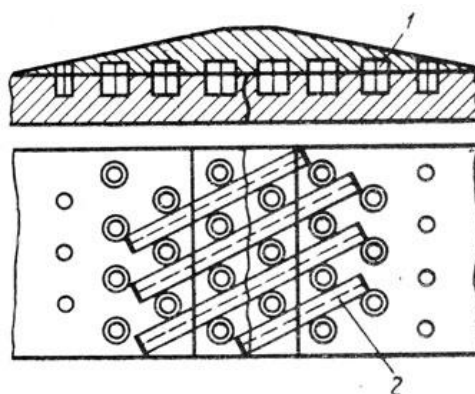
Схема расположения стальных связей в металле шва при холодной сварке чугуна: 1 - шпильки, 2 - стальные связи
